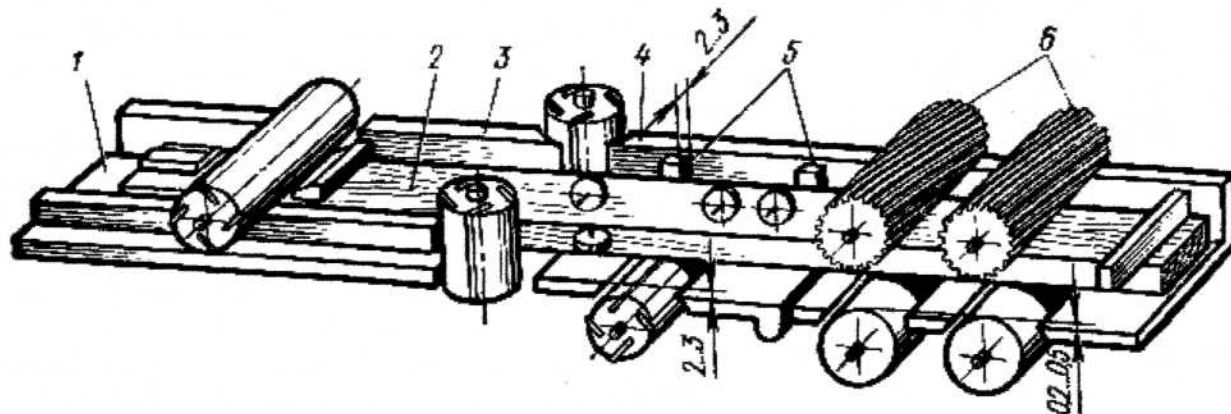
Схема настройки четырехстороннего продольно-фрезерного станка по шаблону:
